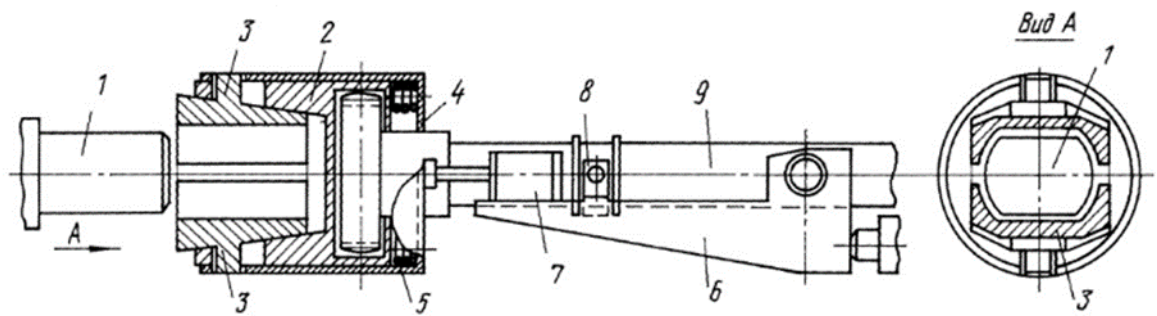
Пристрій з'єднання прокатного валка зі шпинделем
